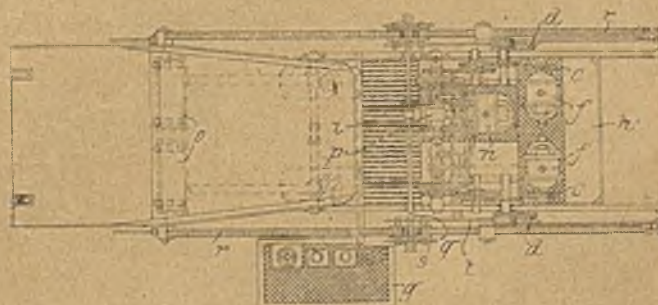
Grundriß der Schaufelvorrichtung von Clausen.
